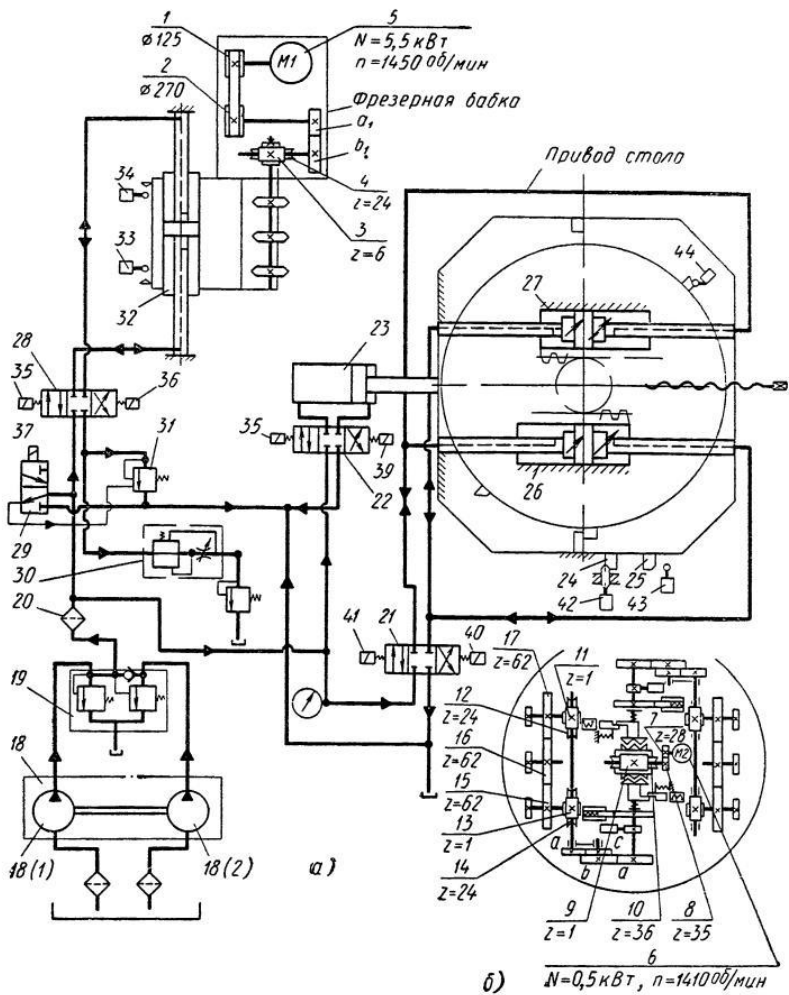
Гидрокинематическая схема зубофрезерного станка ЭЗ-40: а) цепь привода; б) механизм деления
